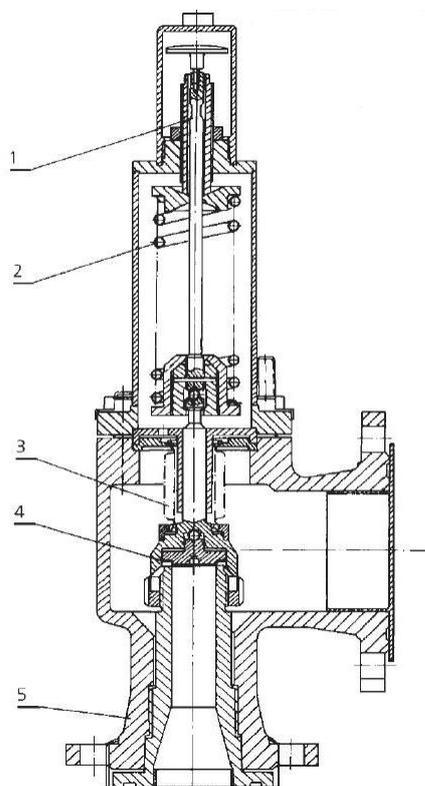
Конструкция предохранительного клапана, где: 1 – винт для настройки; 2 – пружина; 3 – сильфон; 4 – золотник; 5 - корпус
